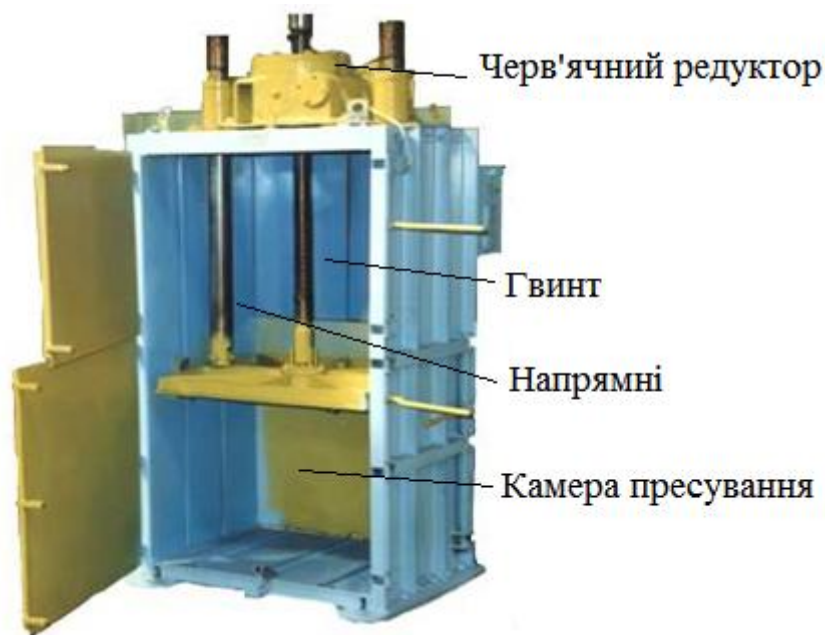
Прес MGP з вертикальним рухом прес-пластини і валу
